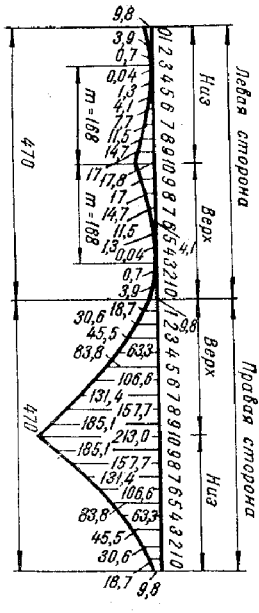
Развертка коша отверстия сварного трюиника.
